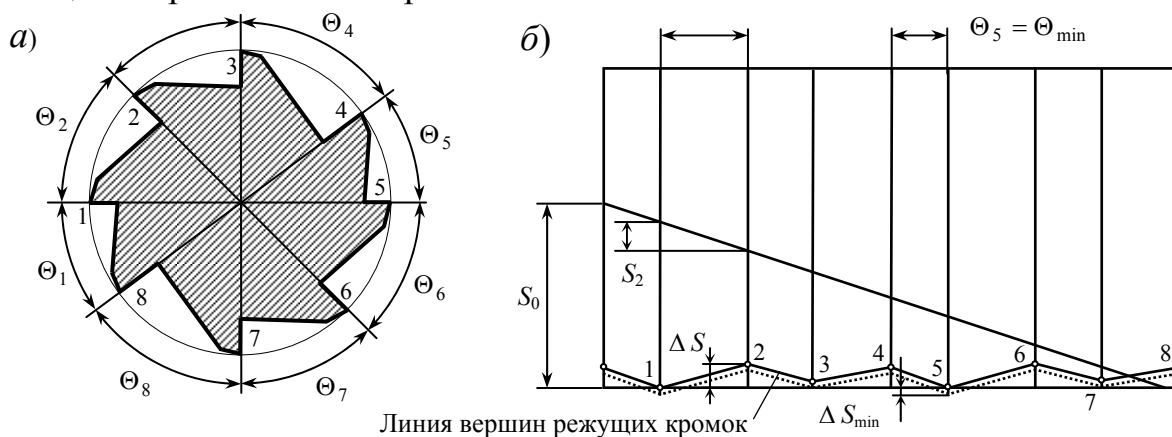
Схема дифференцированной заточки развертки с неравномерным распределением зубьев:
